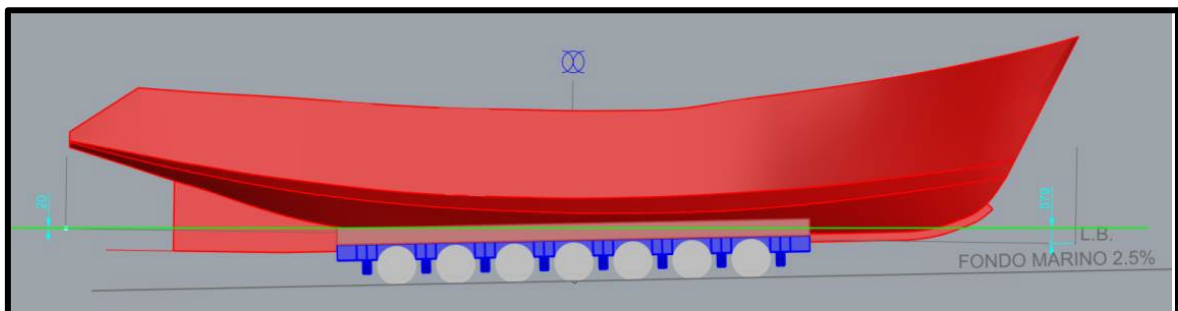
Conjunto Buque-Carreta antes de salir del mar.
